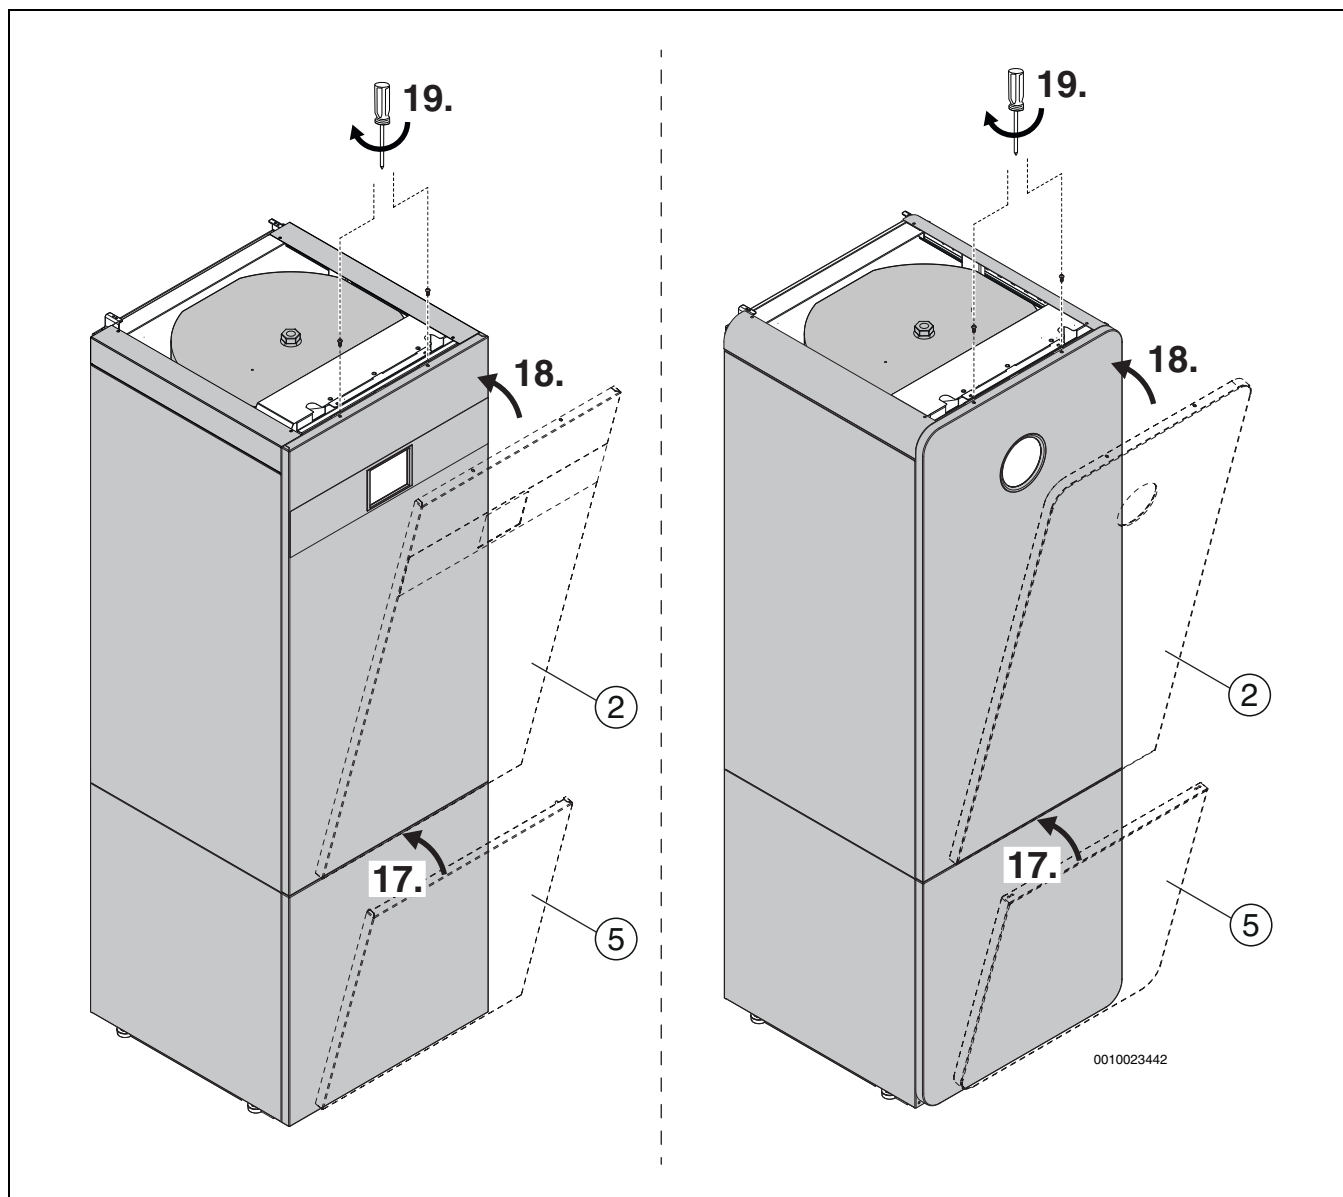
Montage des panneaux avant avec cache carré ou rond
